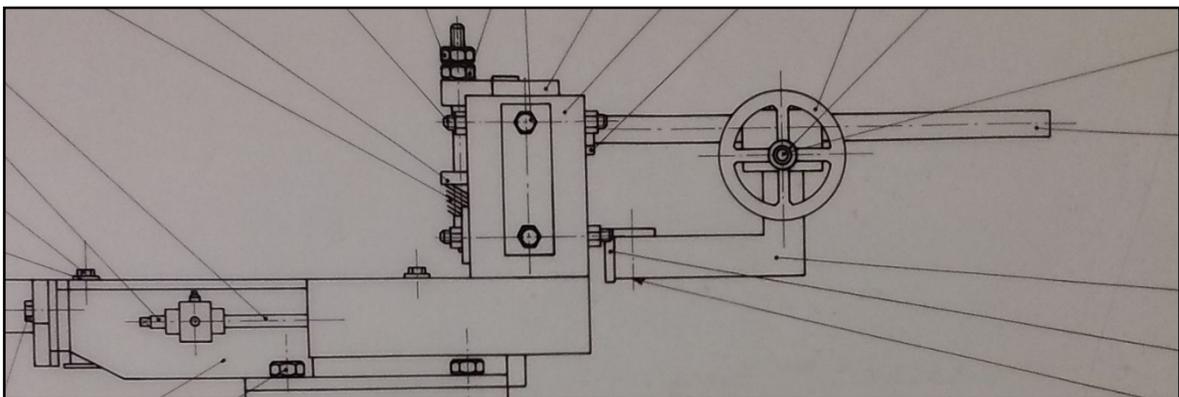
Vista lateral de las barras guías del plano A0-500 Conjunto cizalla mecosoldada.
